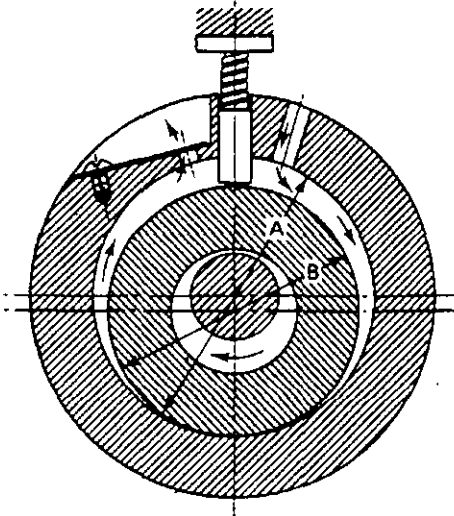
Compresor rotatorio de pistón rodante. (Cortesía de ASHRAE.)
